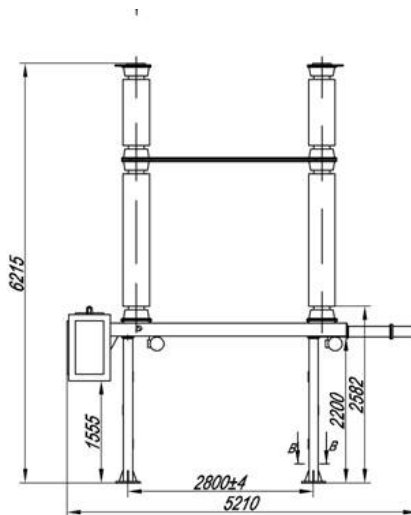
Внешний вид и габаритные размеры – ВГТ 220
